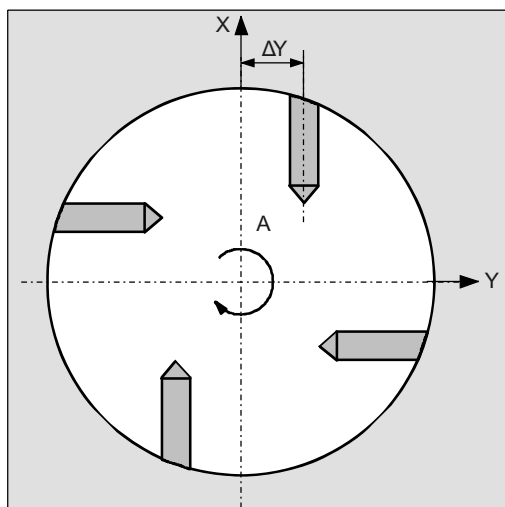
Ось Y располагается не по центру над цилиндром
